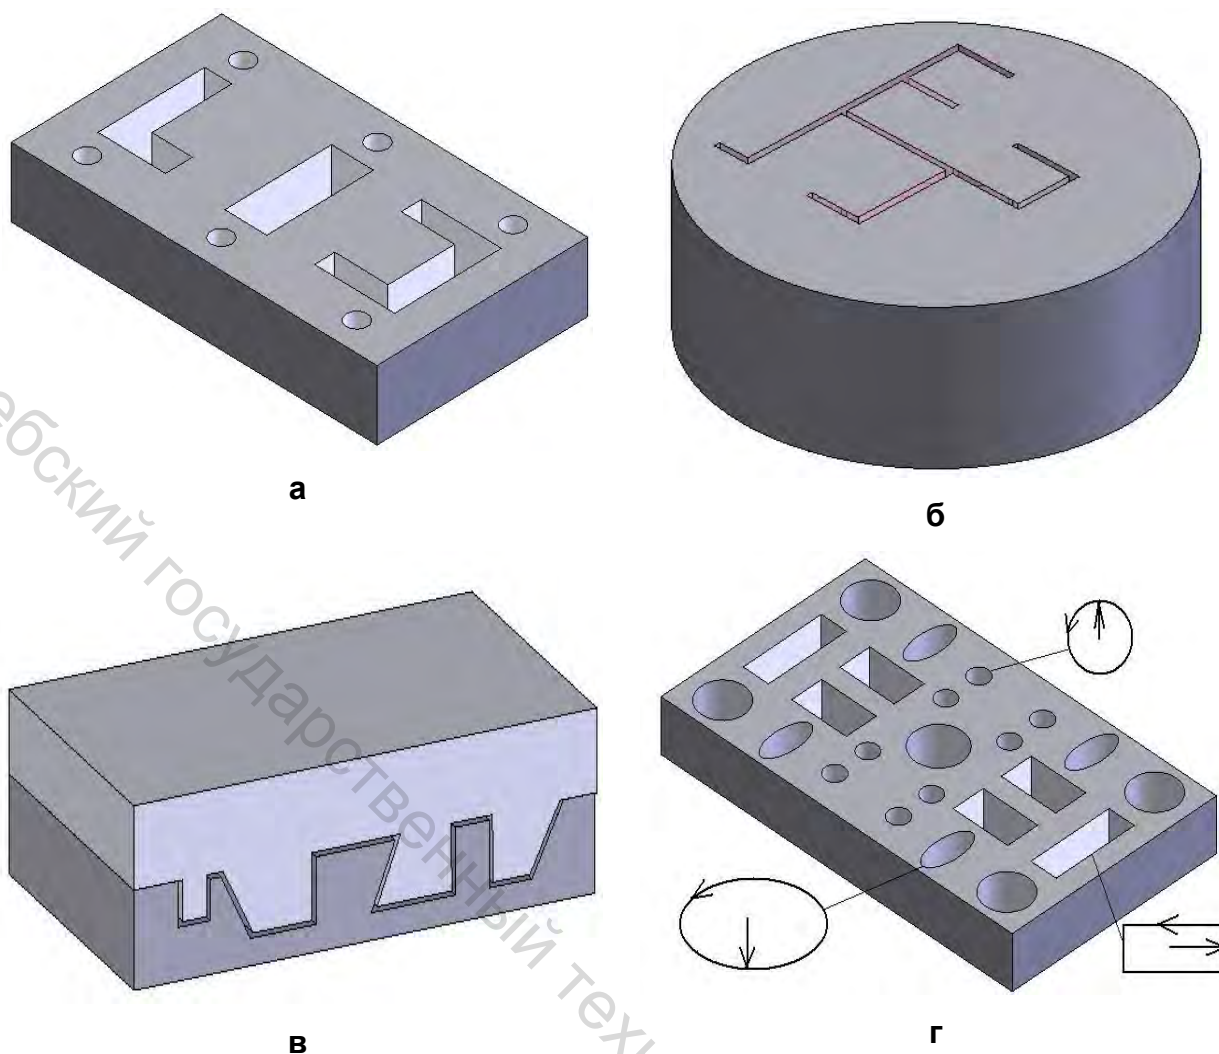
Примеры вырезной обработки деталей различного назначения: а – матриц вырубных и пробивных штампов, б – фильер для экструзии, в – полостей в вытяжных формах, г – деталей из специальных сплавов
